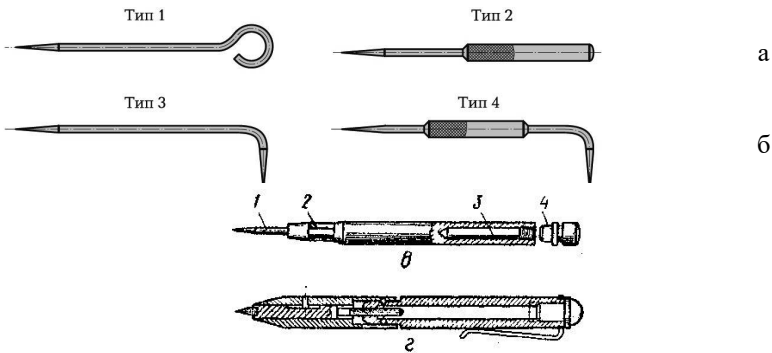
Рисувалки: а – кругла; б – з відігнутих кінцем; в – зі вставними голками; 1 – голка; 2 – корпус; 3 – запасні голки; 4 – пробка; г– кишенькова
